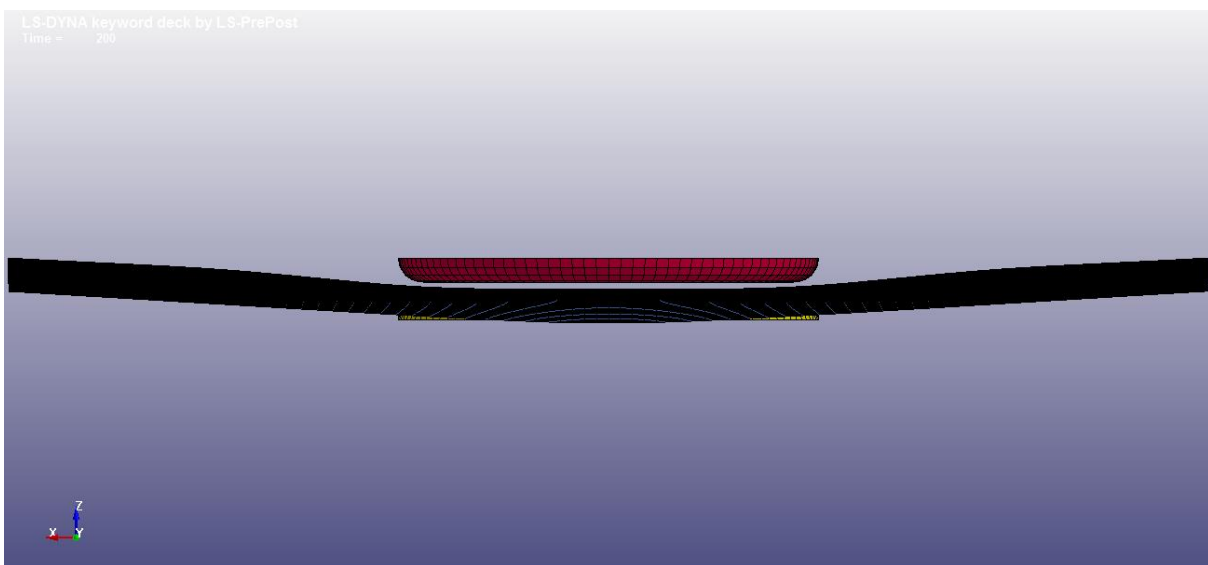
entstandene Blechgeometrie, nachdem sich die Werkzeugbacken wieder in ihrer Ausgangsposition befinden (Seitenansicht)
